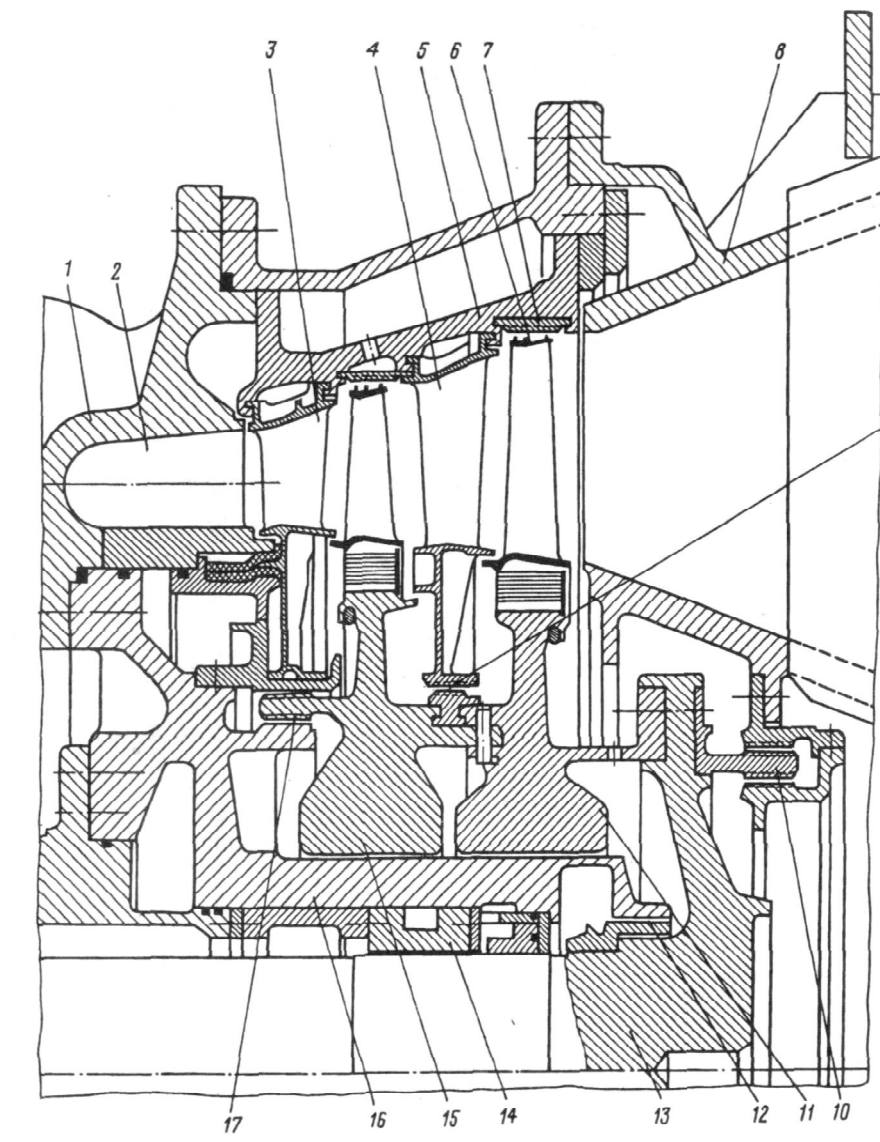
Кинематическая схема детандр-генераторного агрегата ДГА-5000
